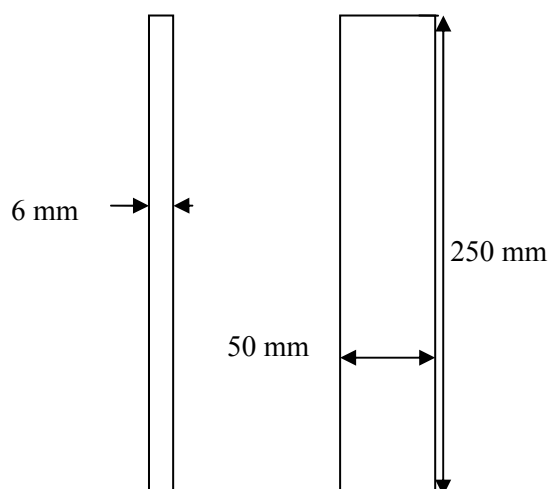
Géométrie des éprouvettes de traction uniaxiale – composite
